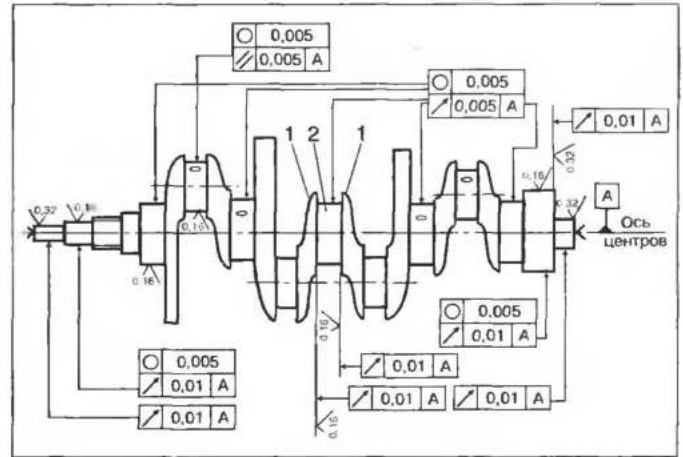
Схема и основные требования к качеству и расположению поверхностей коленчатого вала:
